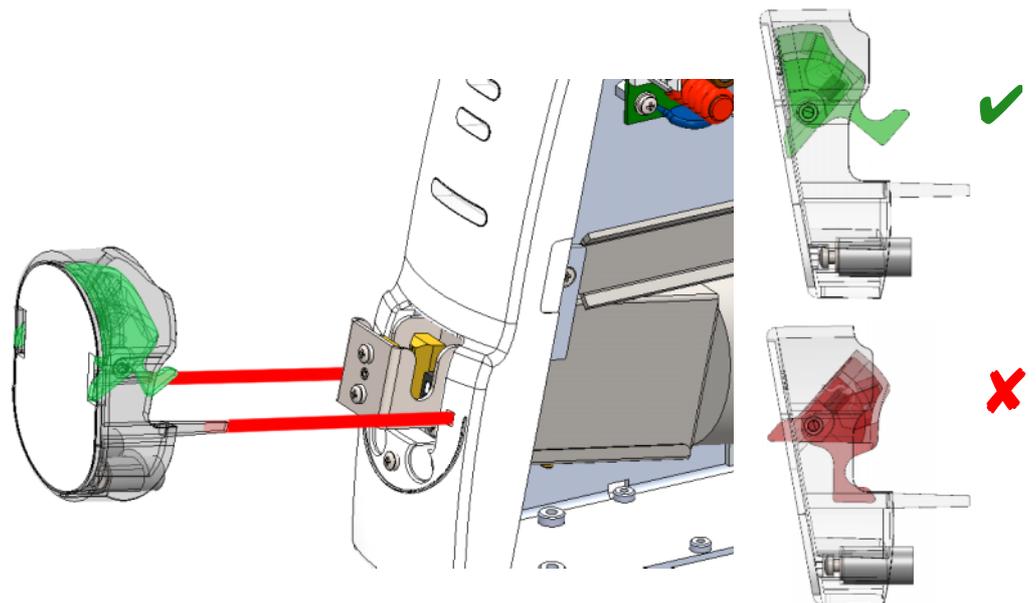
Tampa do sistema de posicionamento de tubos: Instalação / desmontagem
